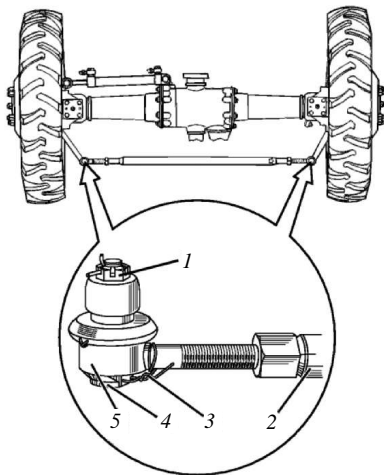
Проверка люфта в шарнирах рулевой тяги: 1 – корончатая гайка; 2 – рулевая тяга; 3 – контровочная проволока; 4 – резьбовая пробка; 5 – шарнир
